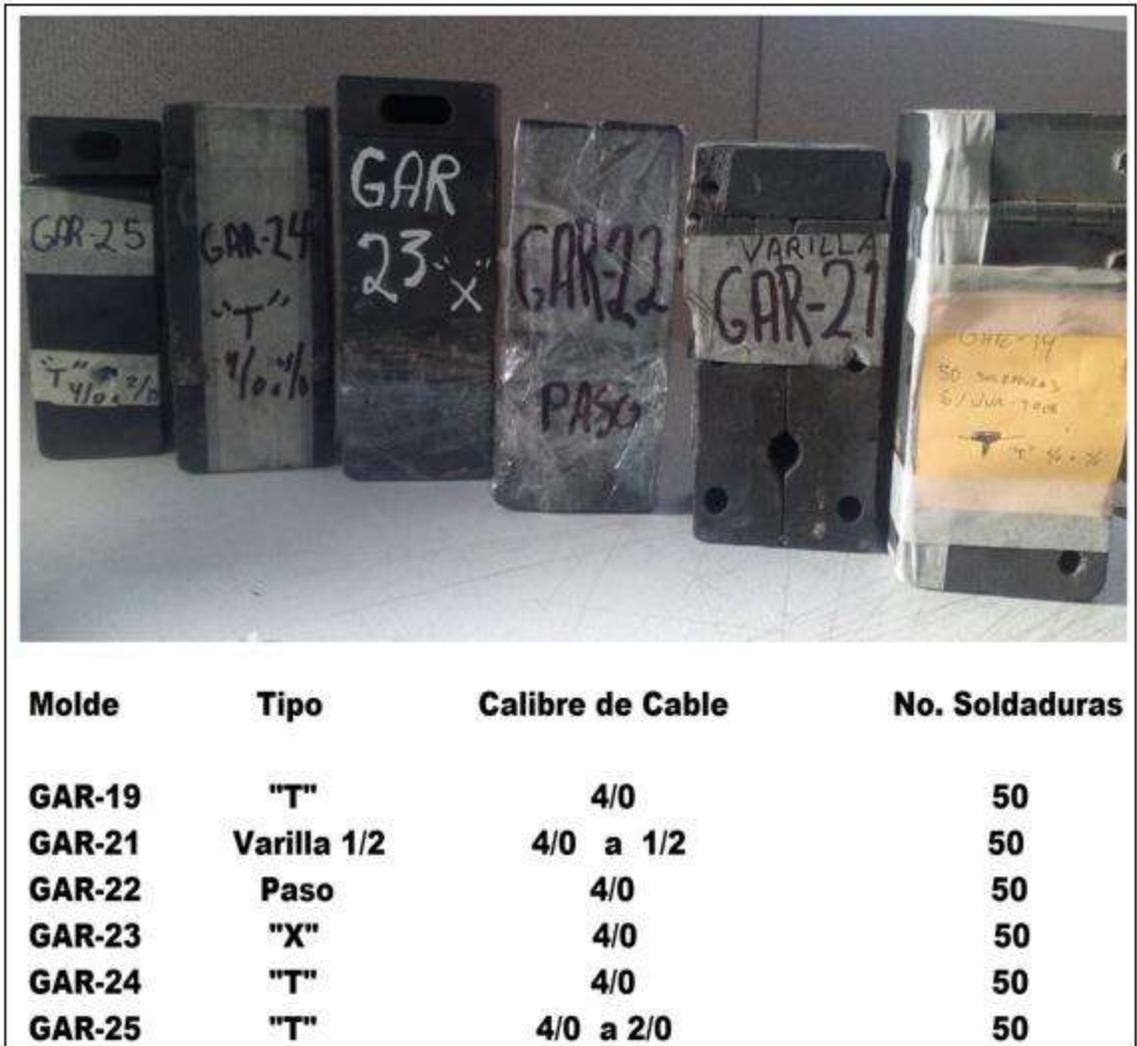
Soldadura Exotérmica trabajo constructivo.
